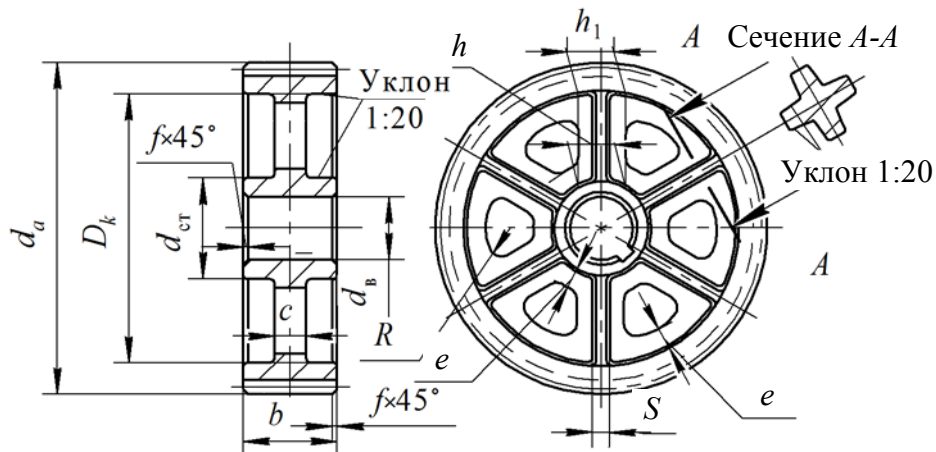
Конструкция цилиндрического зубчатого колеса со спицами
